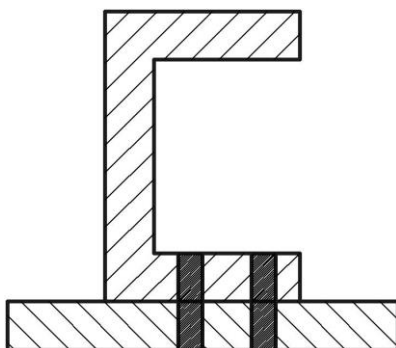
Соединение точечной сваркой полки с коробкой
